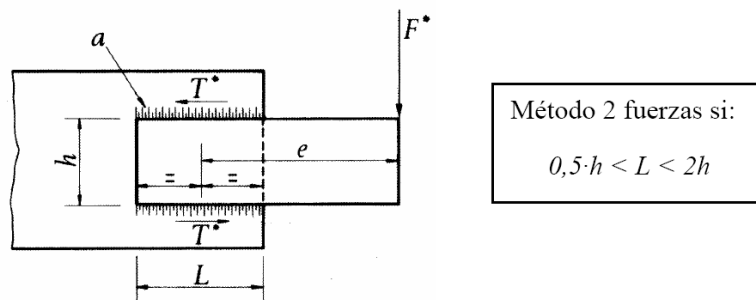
SOLDADURAS LATERALES SOMETIDAS A TORSIÓN Y CORTANTE
